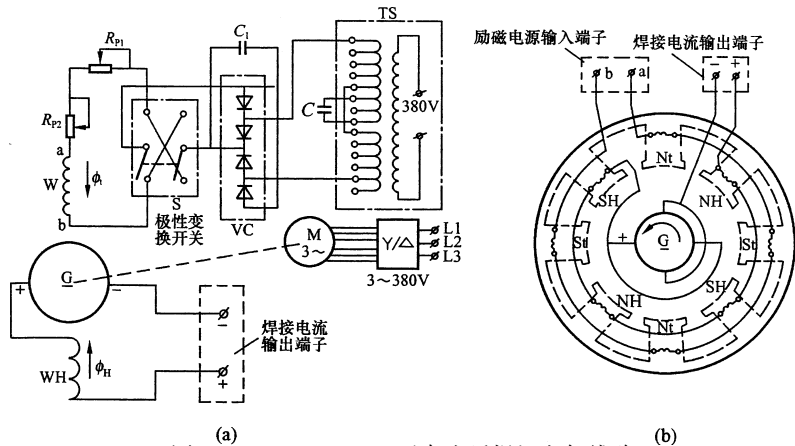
AX4-300 型直流弧焊机电气线路
